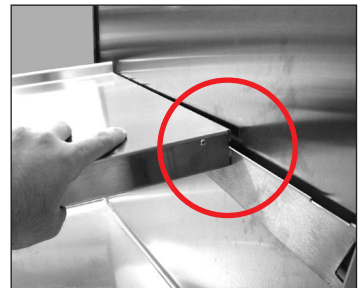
Die Bodenträger in der gewünschten Höhe in die Stangen einhaken.
